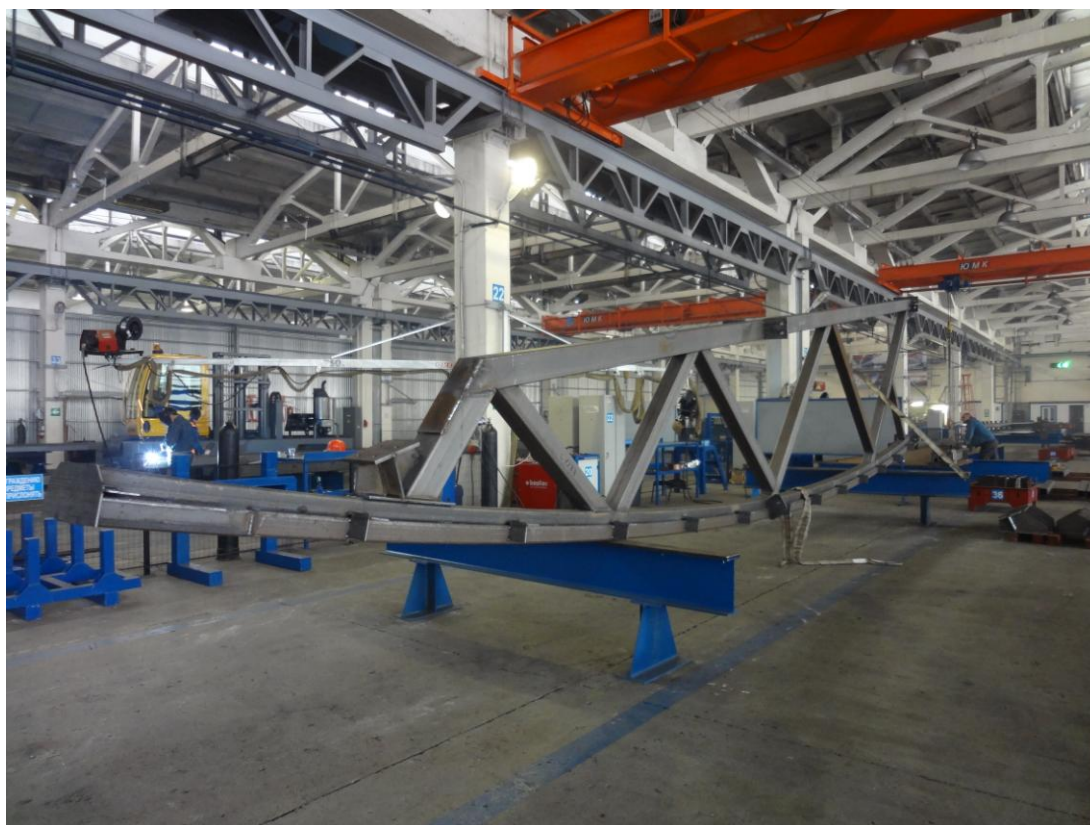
Металлоконструкция фермы из гнутой трубы для склада ООО «Кровельный центр»
